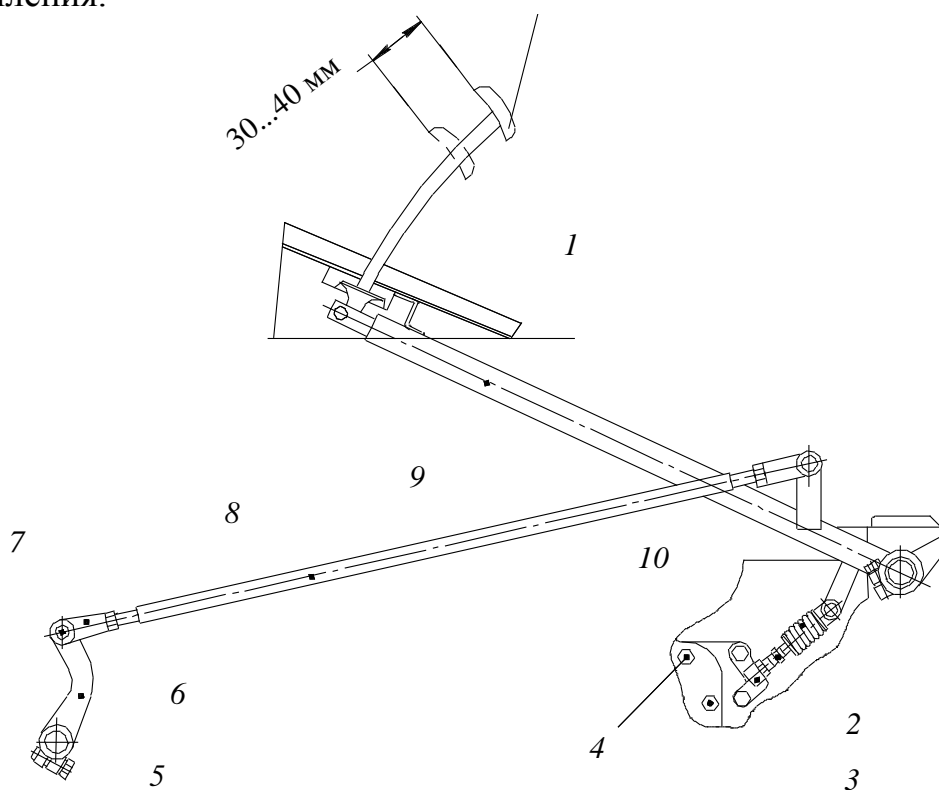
Проверка и регулировка сцепления: 1 – педаль; 2 – регулировочный болт сервоустройства; 3 – кронштейн; 4 – болт крепления; 5 – рычаг; 6 – палец; 7 – вилка; 8 – тяга; 9 – рычаг; 10 – пружина сервоустройства
